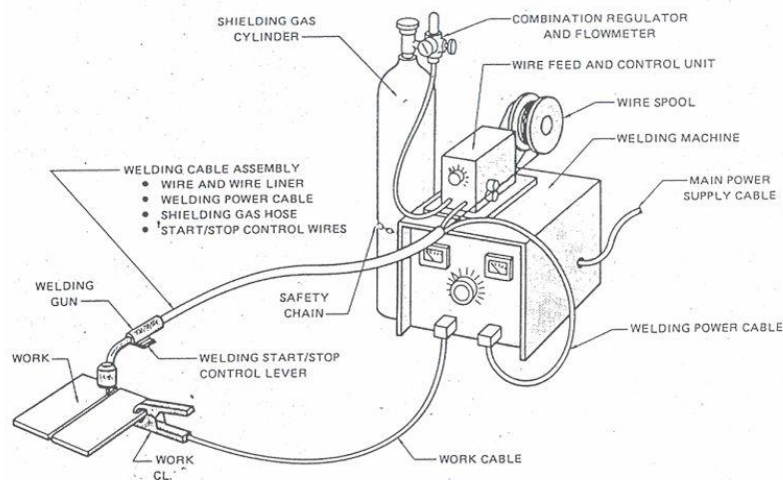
Máquina de Soldadura Semi-Automática Mig/Mag (Shariffuddin, 2015)
